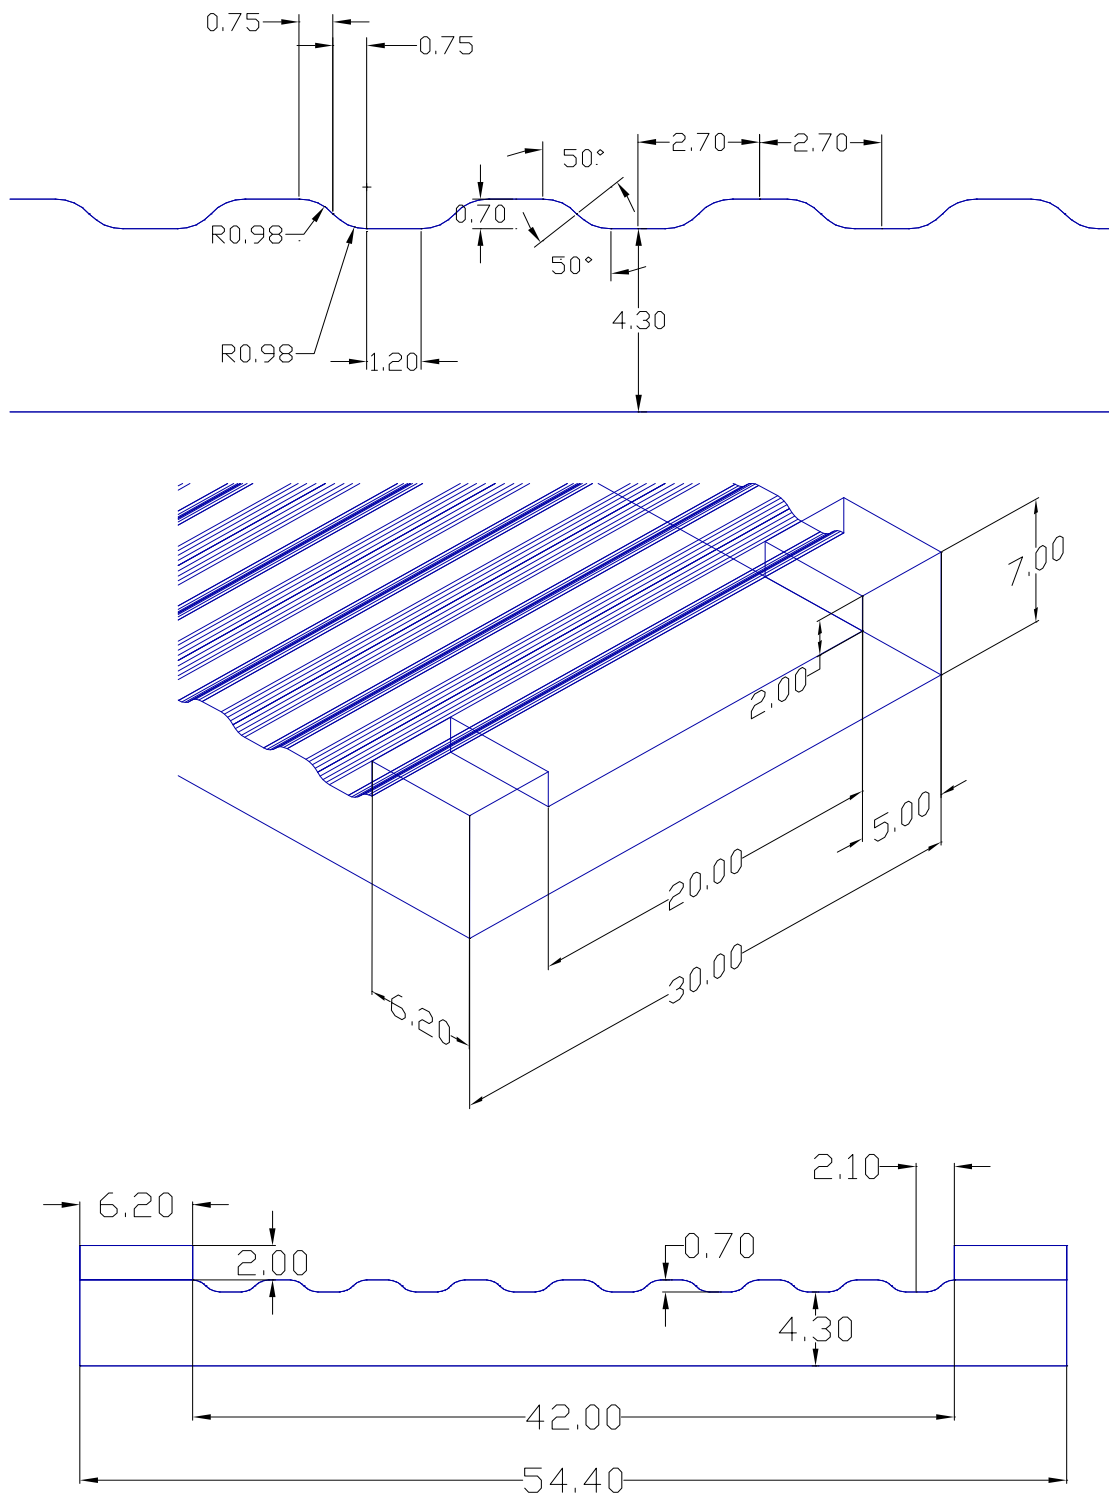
Dimensionnes de la pièce inférieure de la matrice usinée pour la mise en forme des rubans Fe-Ni. Les dimensions sont en mm et les angles en degrés.
